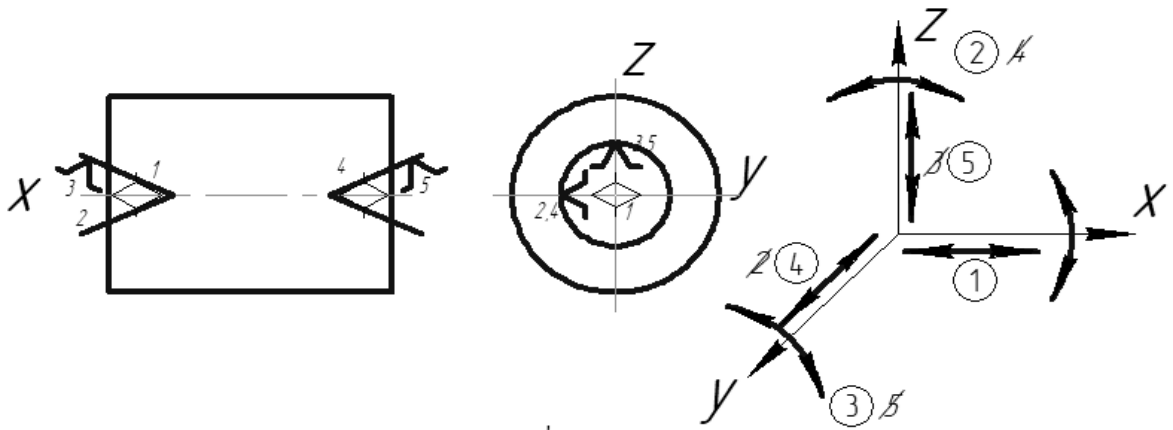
Базування циліндричної заготовки у центрах
